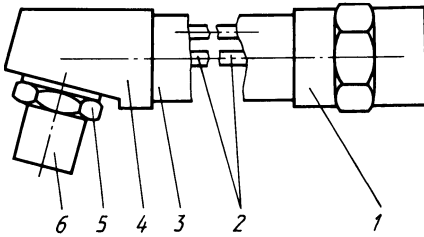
Удлинитель общего назначения: 1 – стыковочный узел; 2 – соединительные трубопроводы; 3 – защитный кожух; 4 – угловая головка; 5 – накидная гайка; 6 – сопловой наконечник.
